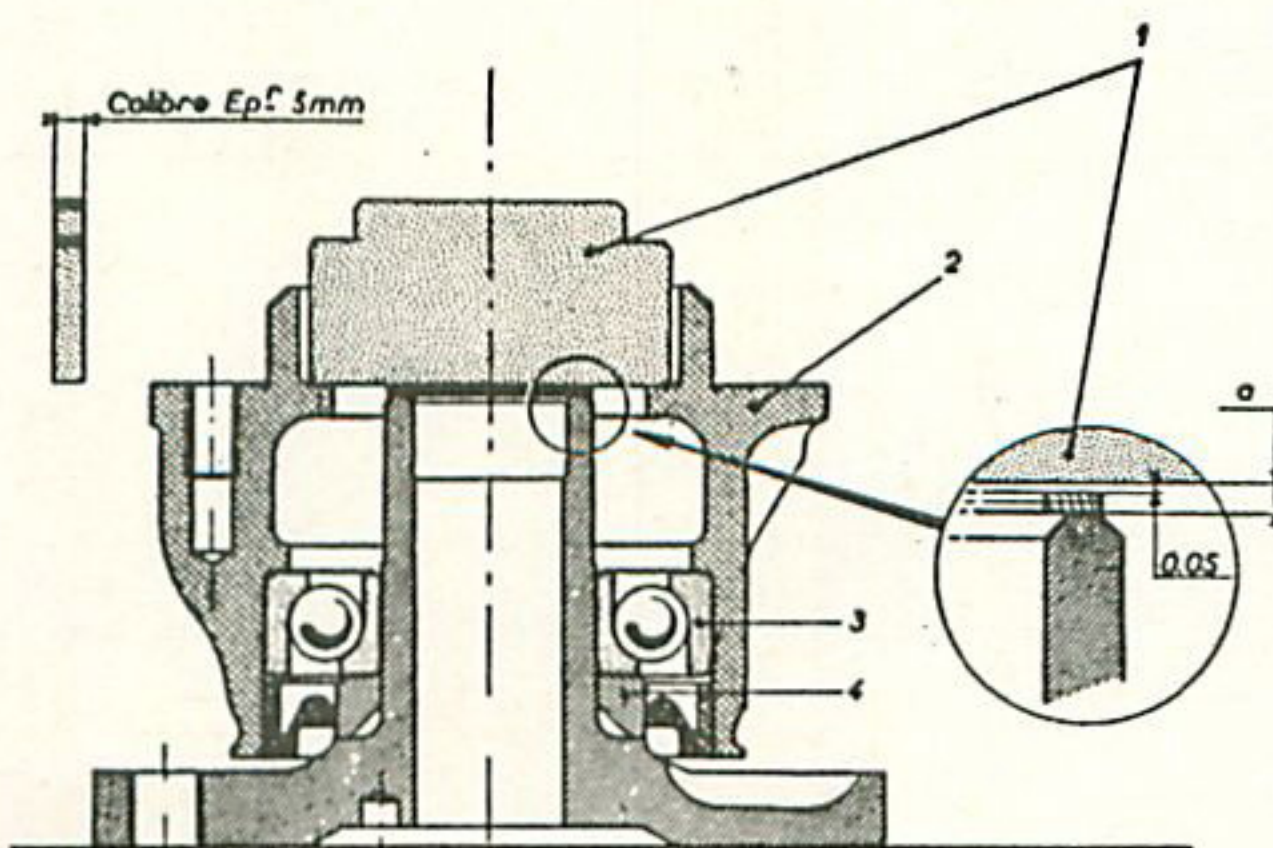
Réglage du jeu latéral du moyeu AV.
